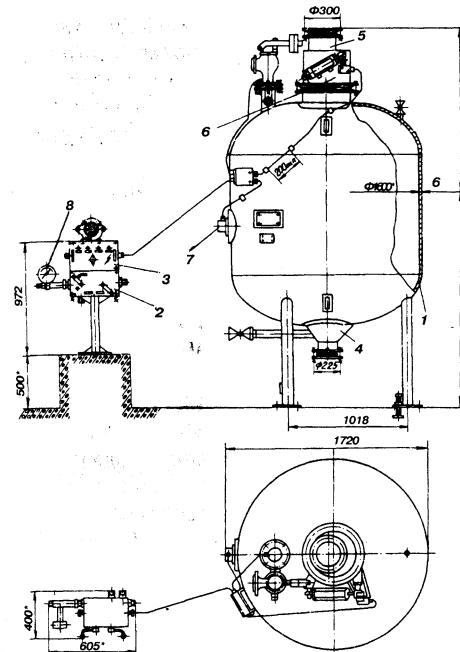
Общий вид передувочного бака Р3-ФПГ:
